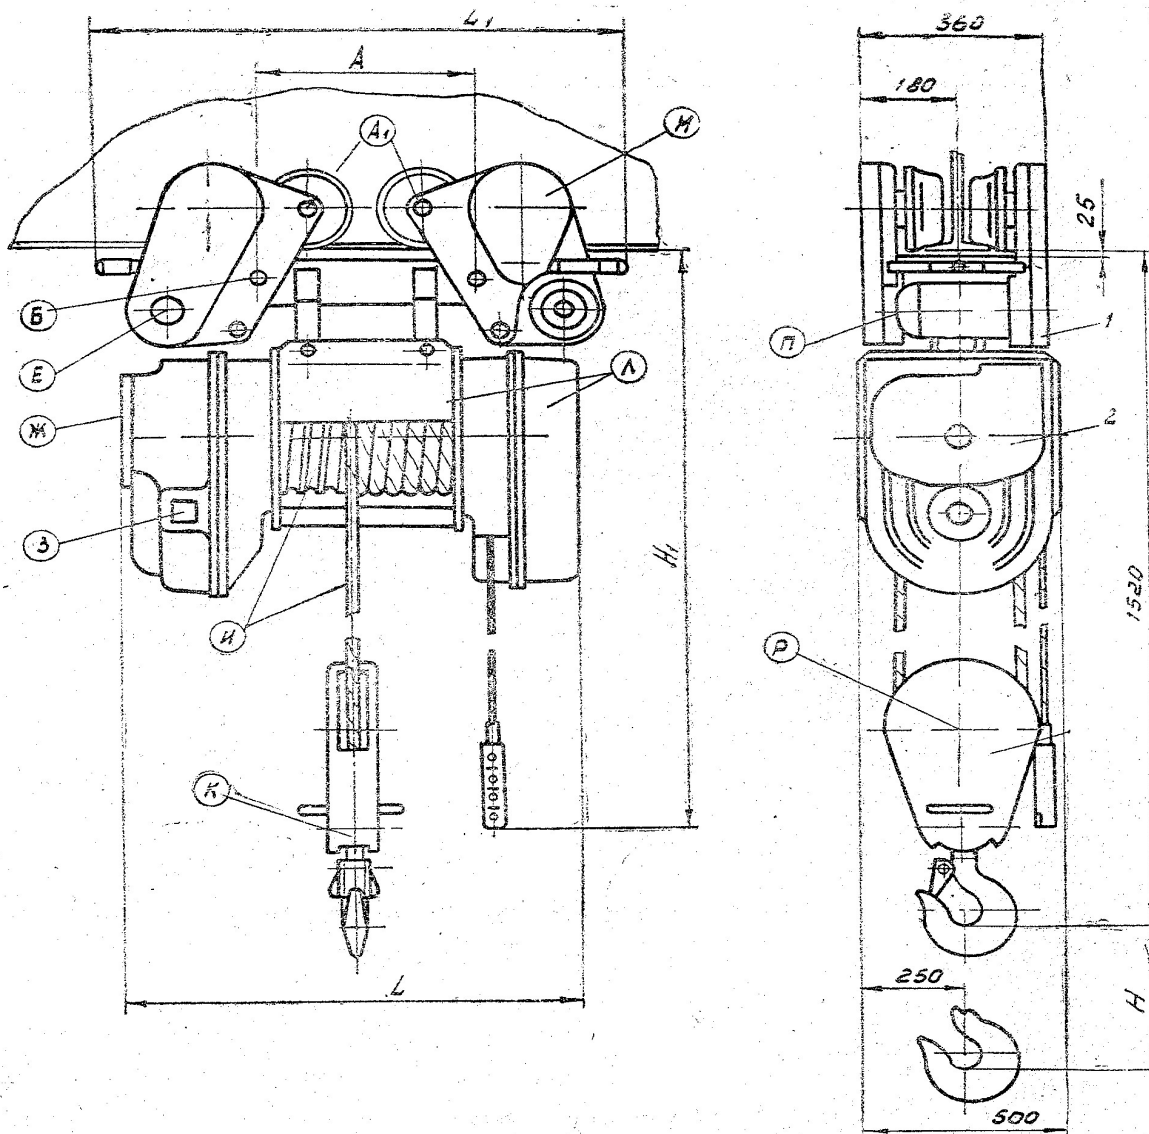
Габаритный чертеж передвижной тали электрической ТЭ500-5 и места смазки
